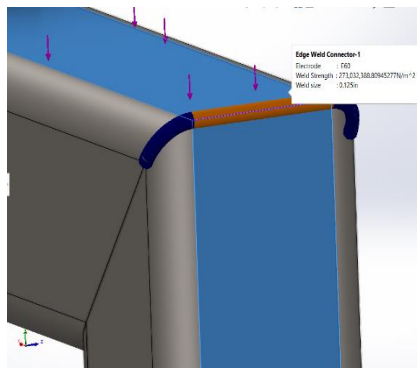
análisis de soldadura realizado en SolidWorks
